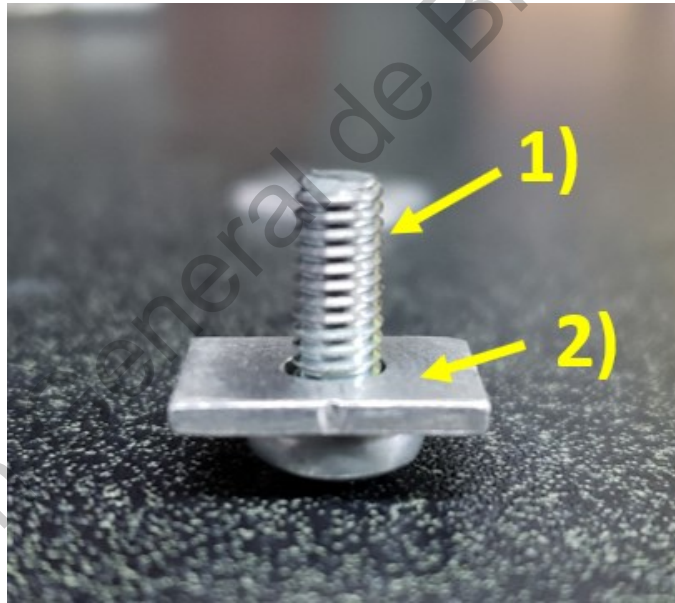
Vista lateral del mecanismo de montaje. 1) Tornillo de sujeción y 2) Holder de aluminio
